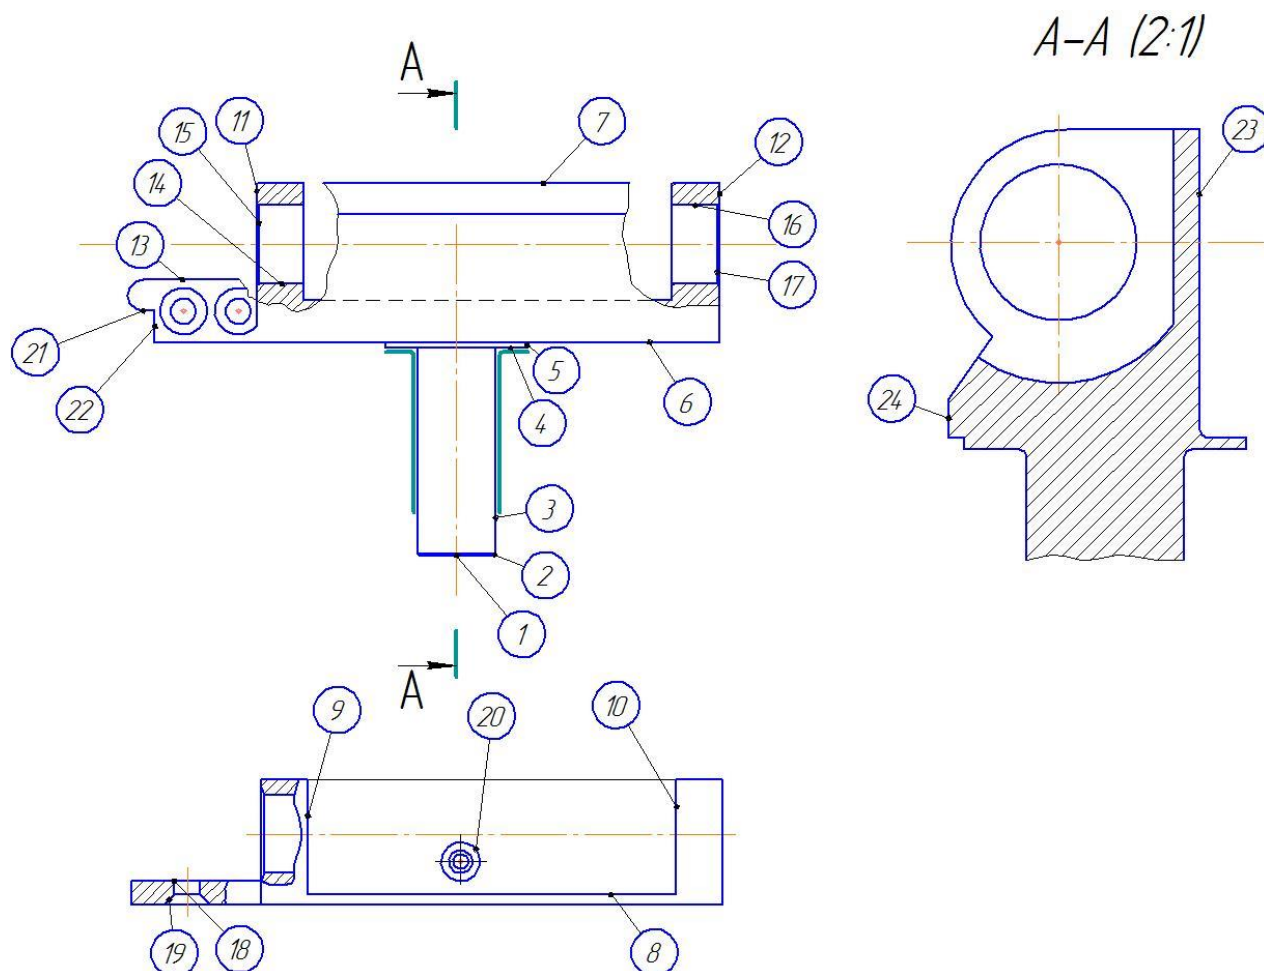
Эскиз детали с номерами обрабатываемых поверхностей
